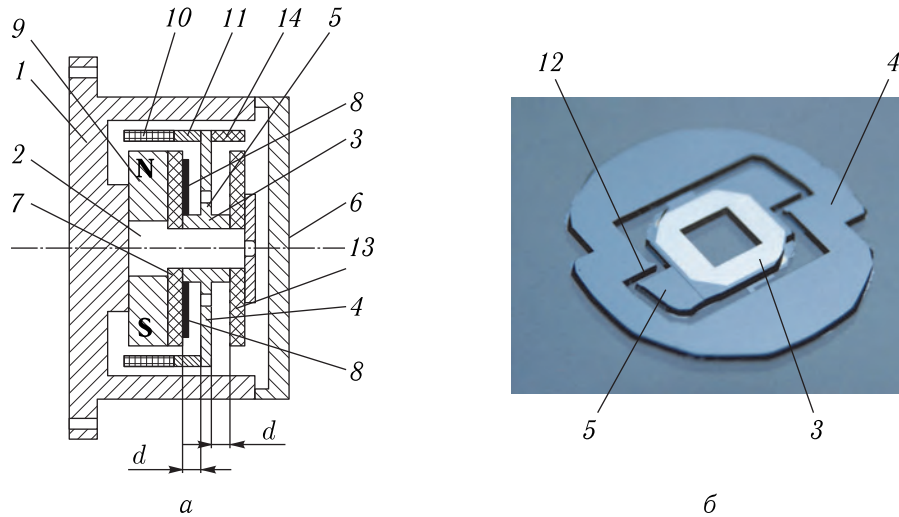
Структурная схема ЧЭ компенсационного акселерометра с кремниевым МУ (а) и образец МУ (б): 1 — корпус; 2 — центрирующая стойка; 3 — кремниевый маятниковый узел; 4, 5 — подвижная и неподвижная части маятникового узла; 6 — крышка корпуса; 7, 13 — пластины; 8 — обкладки конденсатора; 9 — постоянный магнит; 10 — катушка индуктивности; 11 — грузы; 12 — балочные упругие подвесы; 14 — дополнительная масса [9]
